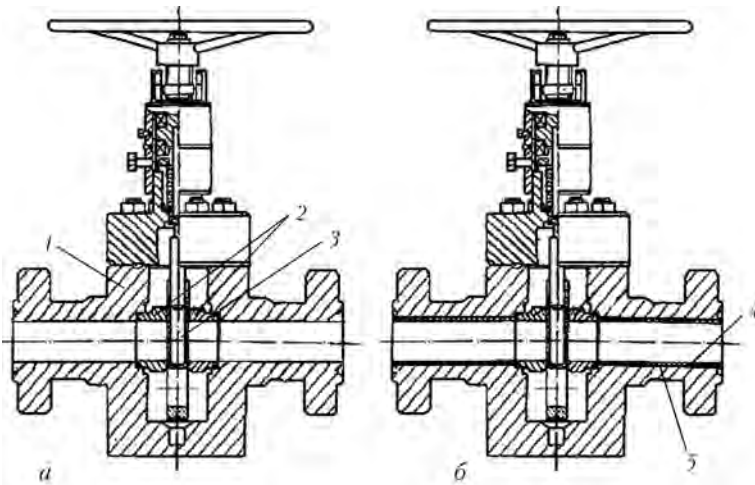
Схема фланцевой задвижки высокого давления с цельнолитым электрошлаковым (*а*) и композиционным (*б*) корпусами: 1 – корпус; 2 – седла; 3 – штибель; 4 – коррозионностойкое покрытие канала; 5 – паяный шов
